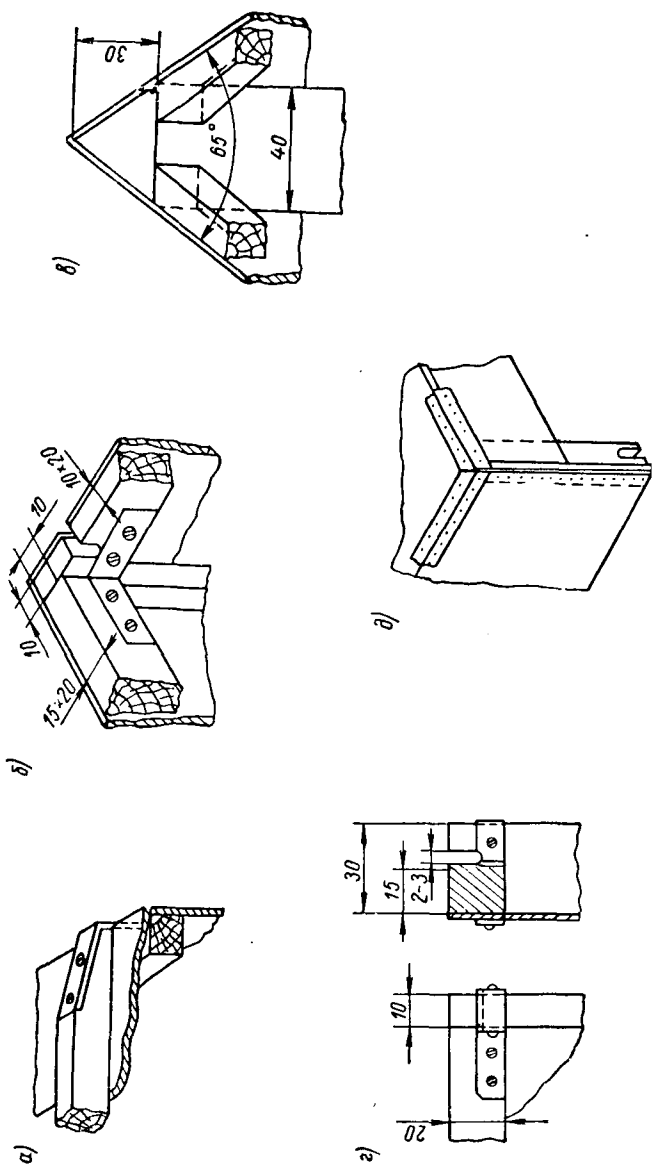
Узлы соединений набора корпуса лодки «Ладога» М1-В: а — оковка наружных днищевых стрингеров; б — соединение бруса и шпангоута; в — соединение бортовых реек у форштевня; г — бортовая ветвь 3 и 4-го шпангоута с пазом для троса; д — окантовка днищевой обшивки (вид снизу).
